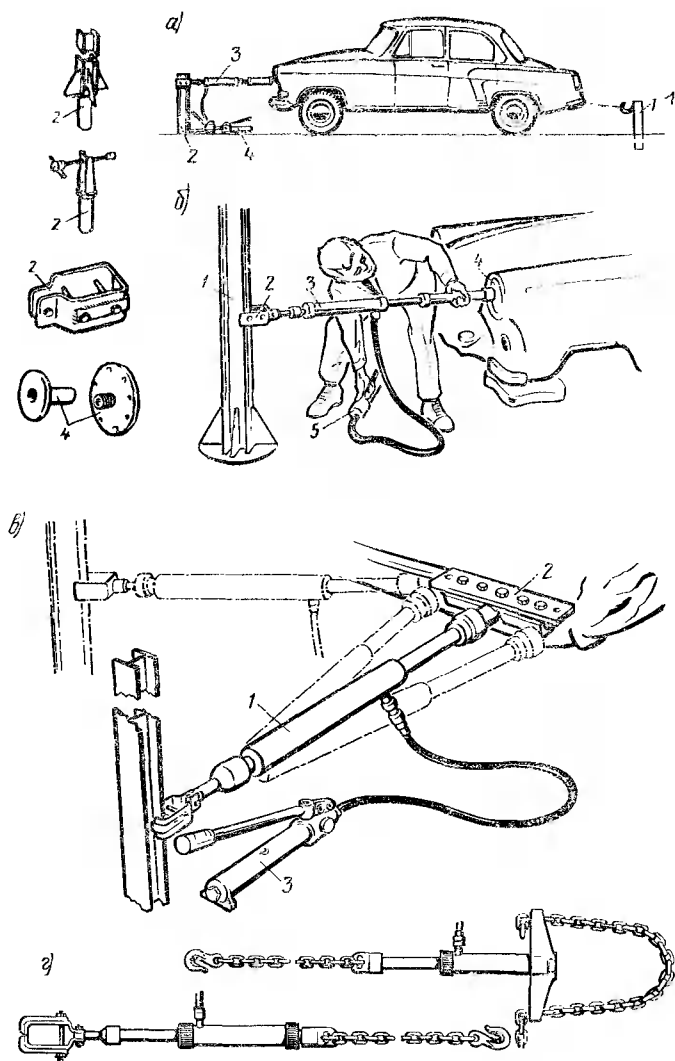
Набор приспособлений для вытягивания вогнутых поверхностей:
